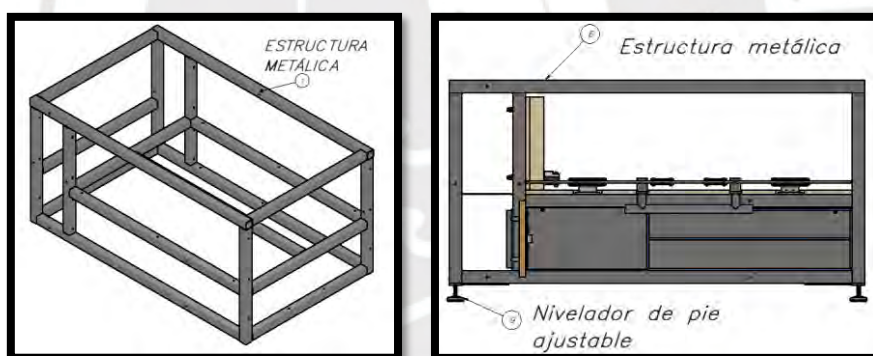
Estructura metálica de la máquina y nivelador de pie ajustable.
